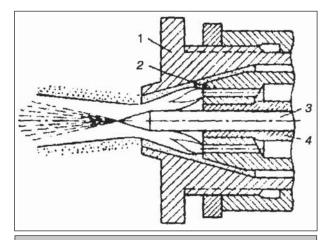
Схема проволочного распылителя: 1 — воздушное сопло; 2 — газовое сопло; 3 — пруток; 4 — направляющая трубка
